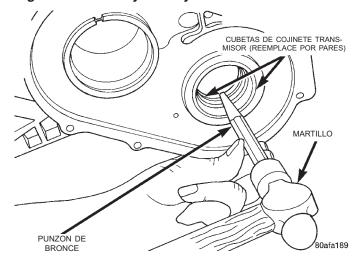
Desmontaje de la cubeta interna del cojinete transmisor
